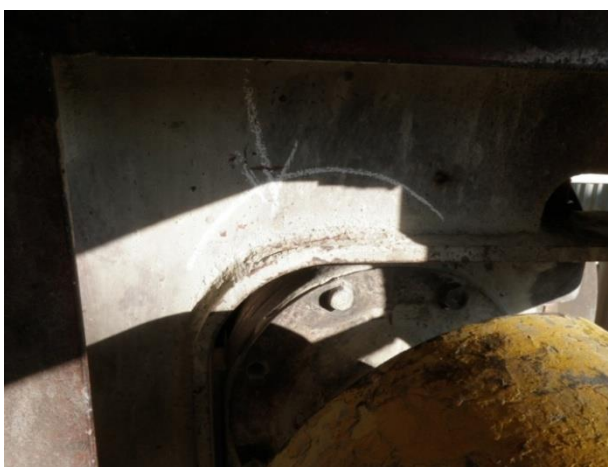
Внутренняя стенка в буксовой зоне приводного ходового колеса. Трещина длиной 70мм в сварном шве крепления гнутого листа к стенке балки.
